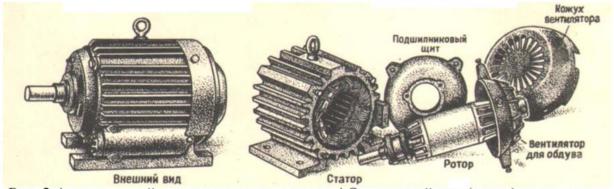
Асинхронный электродвигатель серии АО, внишний вид (слева) и элементы его конструкции (справа).
